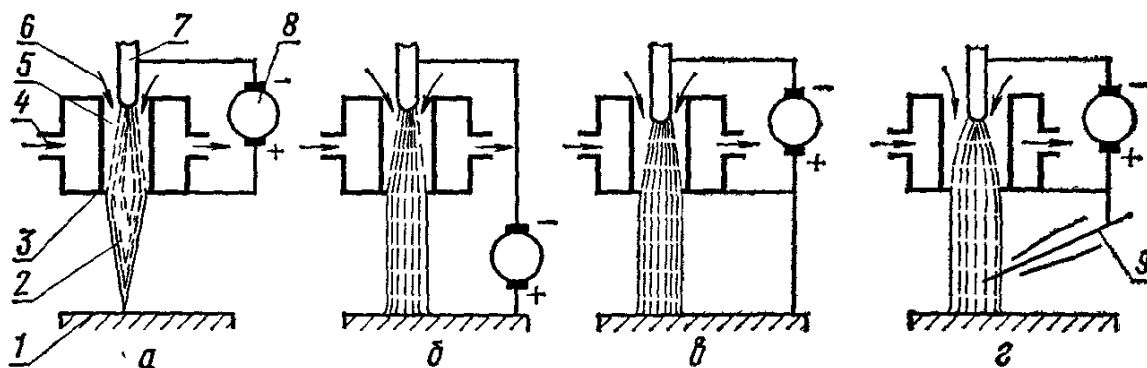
Можливі схеми ведення плазмового наплавлення і різання металу:
